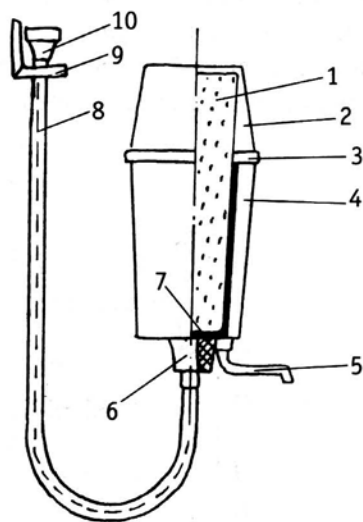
Фильтр «Родник-3М»: 1 — фильтр-патрон; 2 — крышка; 3 — пояс; 4 — корпус; 5 — излив; 6 — гайка; 7 — прокладка резиновая; 8 — шланг; 9 — вилка подвески; 10 — насадка
